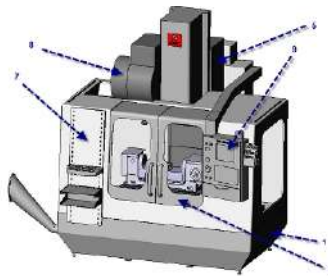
Корпус вертикально-фрезерного верстата із ЧПУ
